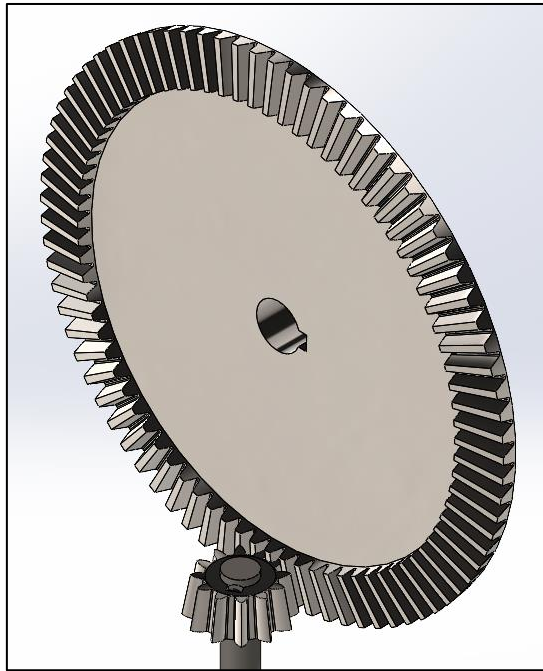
Conjunto engranajes cónicos. Fuente propia.
